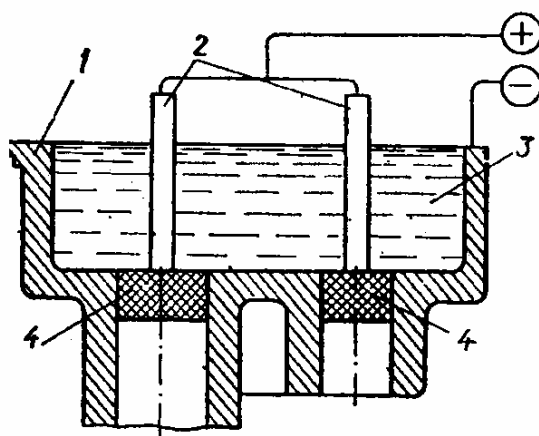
Схема електролітичного нарощування внутрішньої поверхні корпуса насоса:
